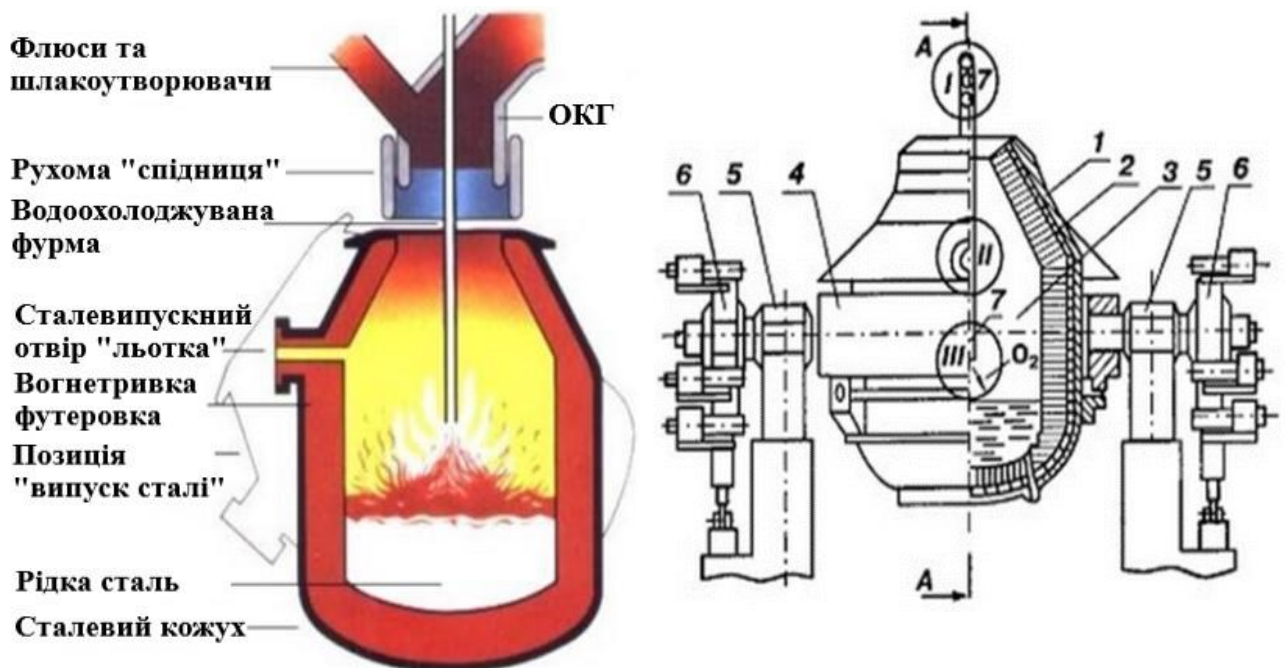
Загальна будова кисневого конвертера верхнього дуття: 1 – корпус; 2 – футерівка; 3 – робочий простір конвертера; 4 – опорне кільце з цапфами і системою кріплення в ньому корпусу; 5 – опорні вузли та станини; 6 – механізм повороту; 7 – киснева фурма з системою кріплення і переміщення.
